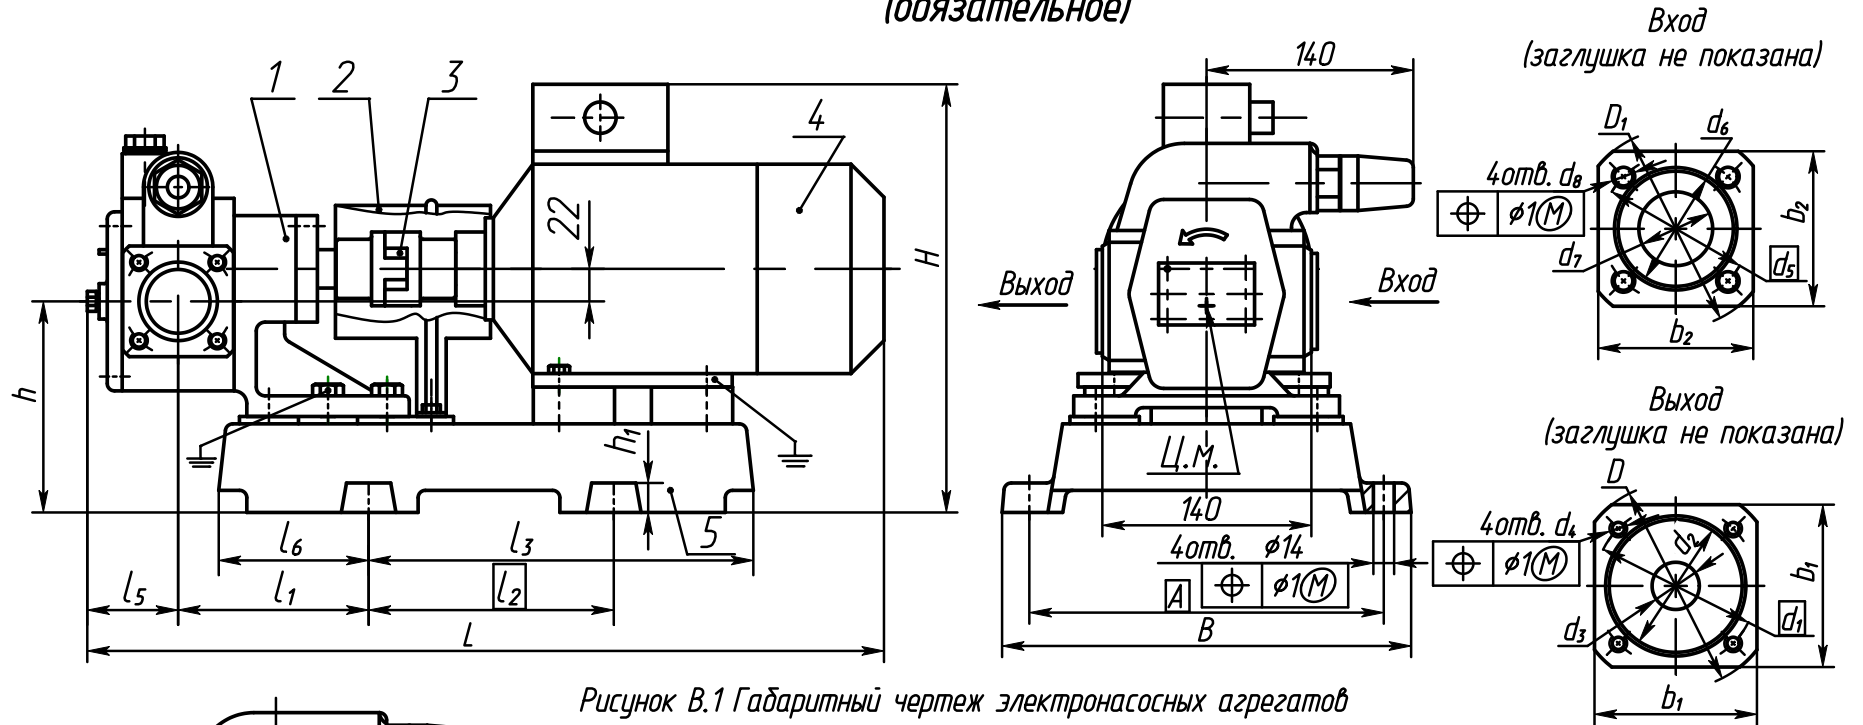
Габаритный чертёж электронасосных агрегатов
